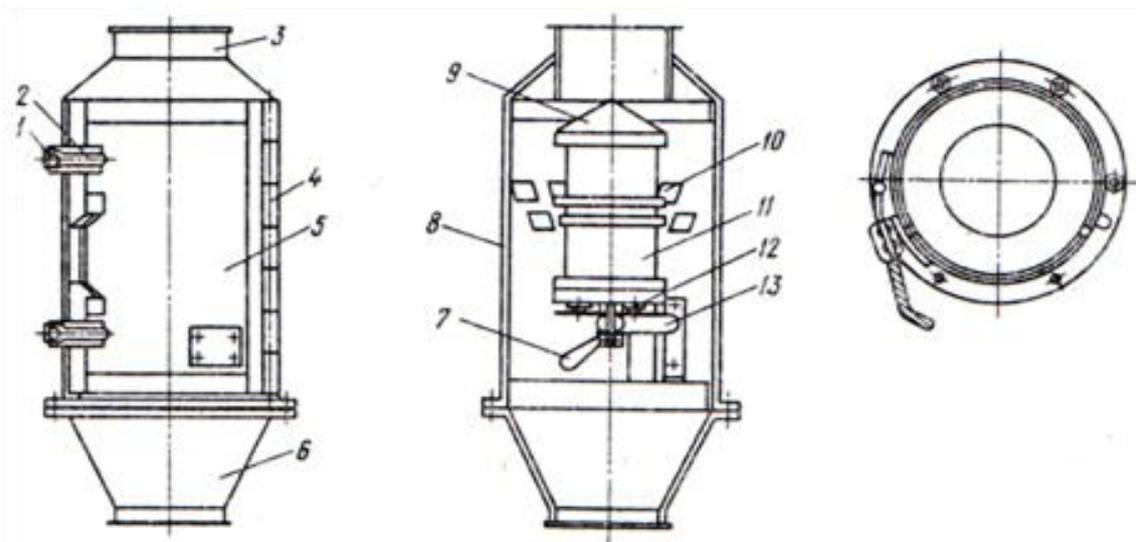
Магнитный сепаратор У1-БММ
